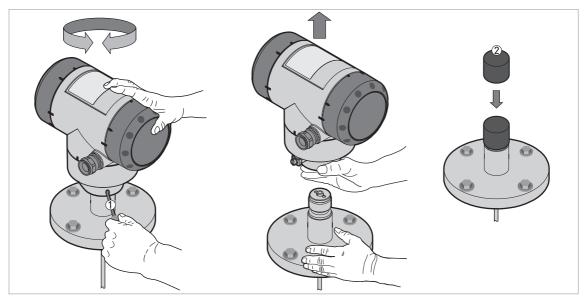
Drehen bzw. Entfernen des Messumformers
